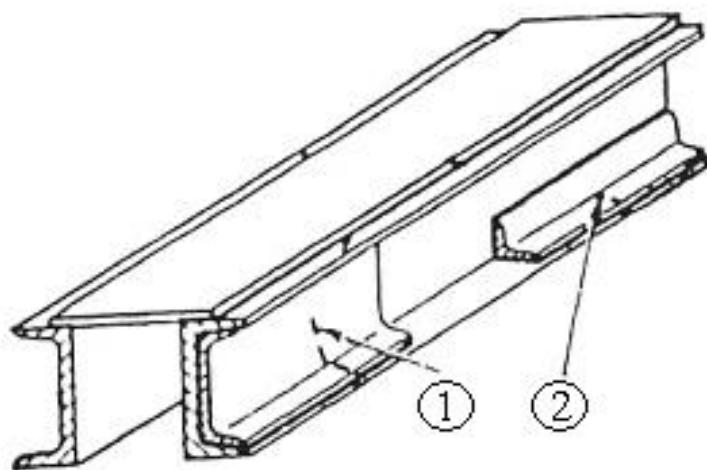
Дефекты балки хребтовой, ремонтируемые сваркой или наплавкой
